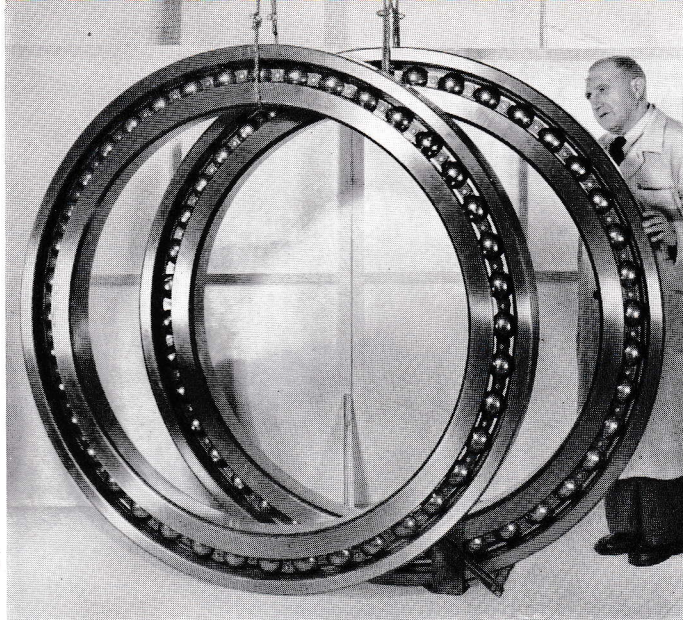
En el engranaje de giro están montados los rodamientos de una hilera de bolas con contacto angular representados en la figura
